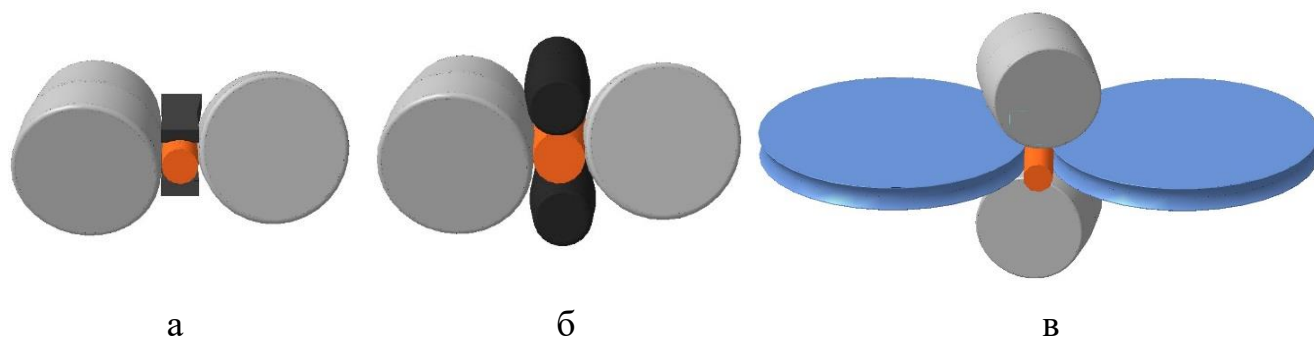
Виды очагов деформации двухвалковых станов винтовой прокатки:
